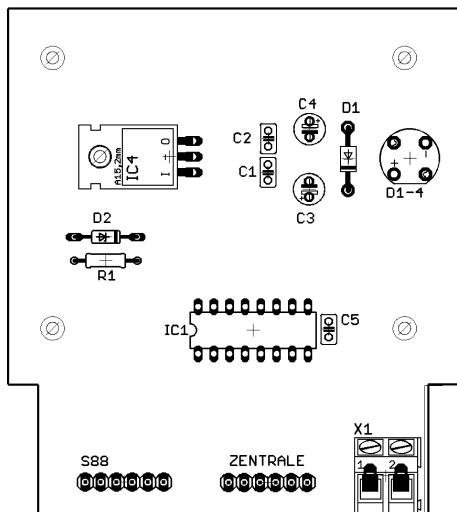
Bestückungsplan - PCB layout - Plan d'implantation - Printplan
